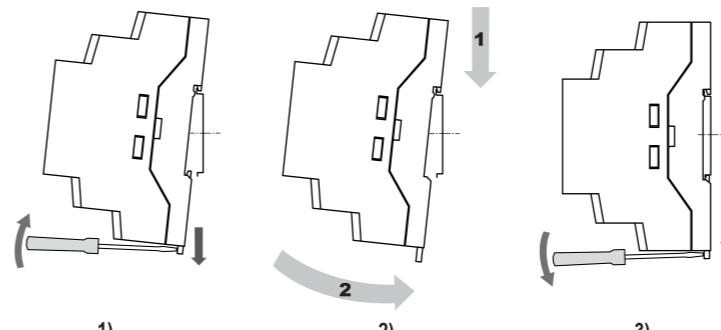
Монтаж прибора с креплением на DIN-рейку
